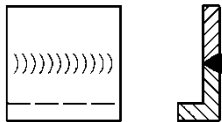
Soldadura en ángulo discontinua
